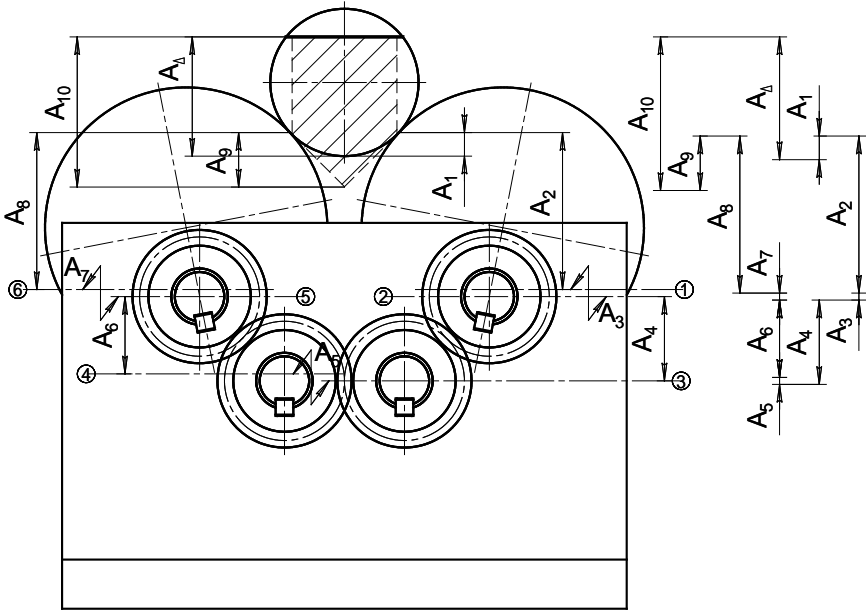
Базуюча призма (патент України № 31416) і розмірний ланцюг для визначення похибки базування вала при фрезеруванні лиски, паралельної до робочої поверхні стола верстата
